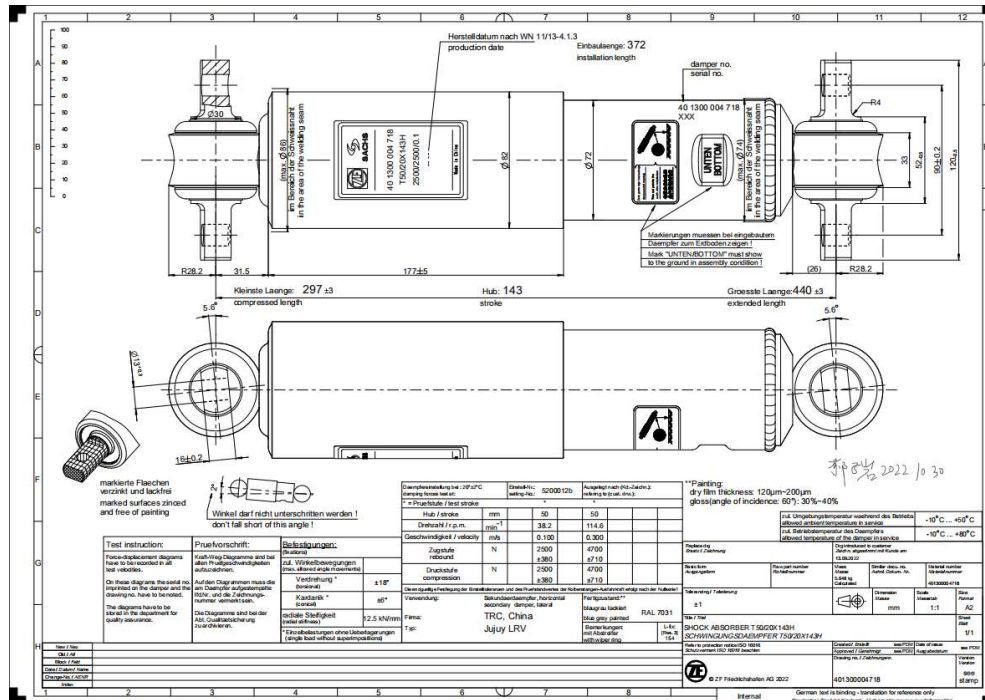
Plano del amortiguador transversal de la suspensión secundaria
